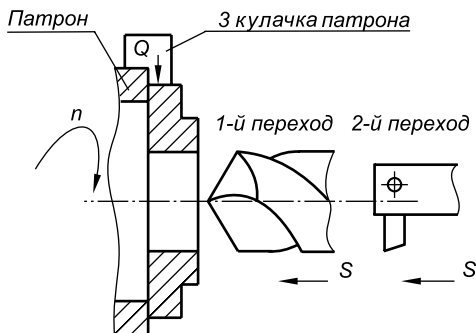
Схема токарно-сверлильной обработки детали типа тела вращения:  $n$  — частота вращения патрона;  $S$  — подача инструмента;  $Q$  — сила закрепления детали
